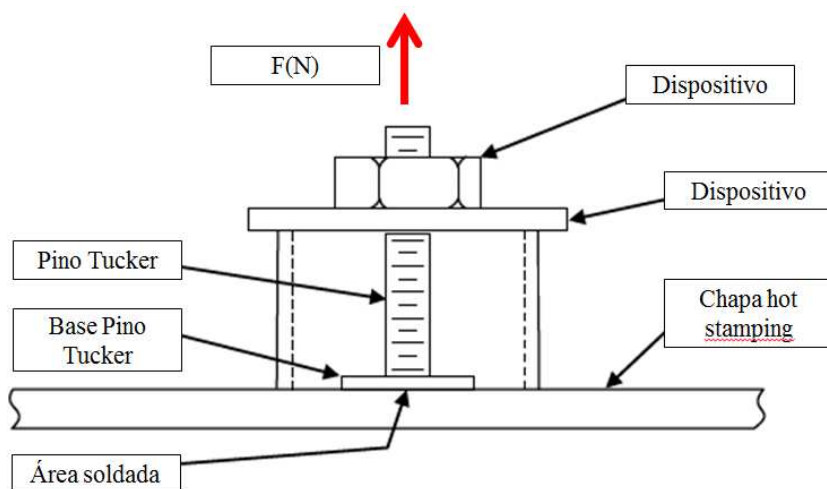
Esquema do ensaio de tração realizado no conjunto soldado Pino/Chapa
